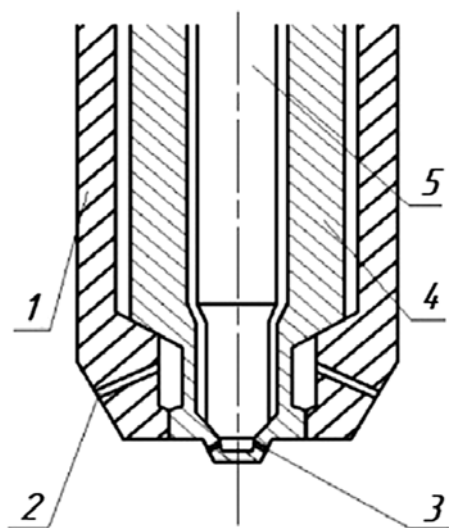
Схема двухтопливной форсунки: 1 — корпус форсунки; 2 — сопла распыления природного газа; 3 — сопло распыления дизельного топлива; 4 — игла форсунки (природный газ); 5 — игла форсунки (дизельное топливо) [6]
